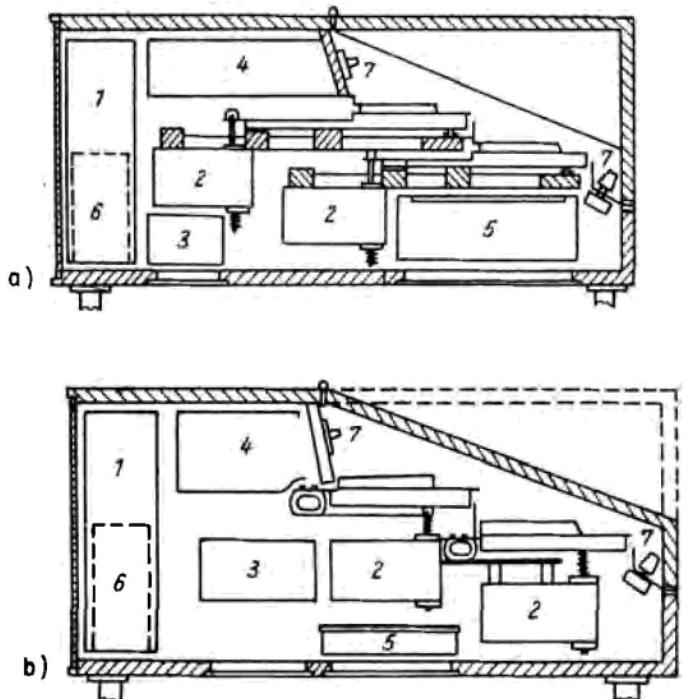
Beispiele für den inneren Aufbau der Instrumente B/1 bis B/3 (schematisch). Bezifferung der Baugruppen wie in Bild 16.10
